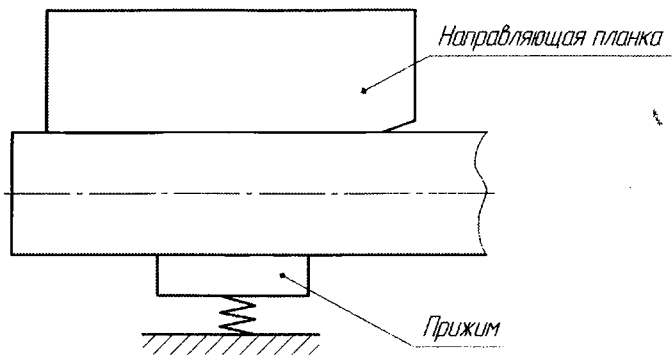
Штамп с ловителем для более точного расположения заготовки
